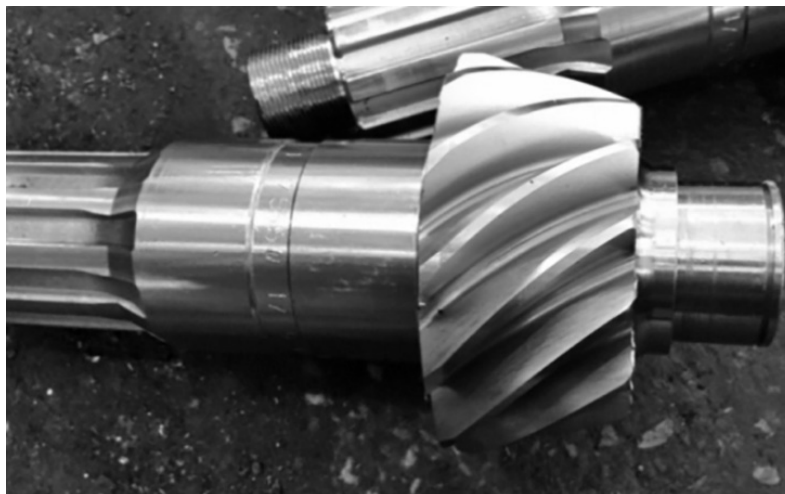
Зубчатые колеса из цементованной стали 20ХНЗМА
